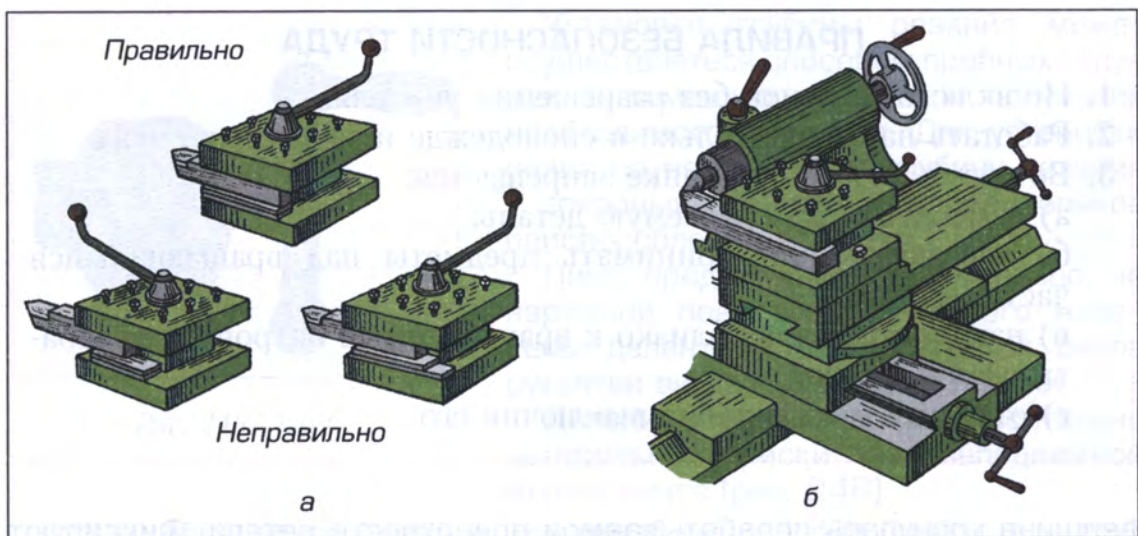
Использование подкладок для центровки вершины резца (а) и проверка качества центровки (б)
